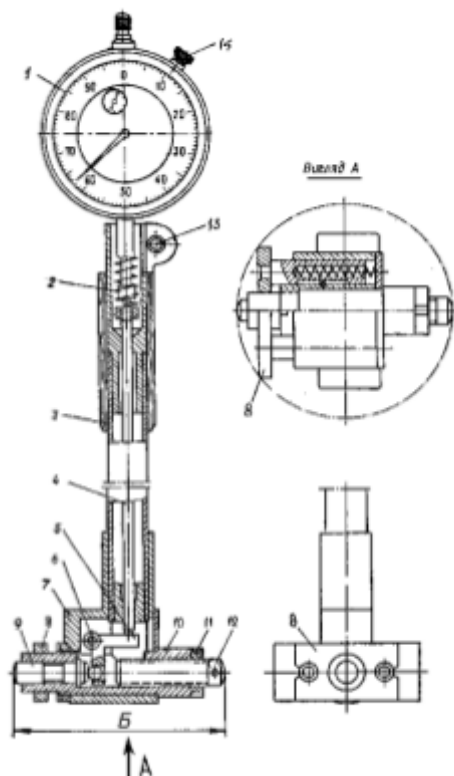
Індикаторний нутромір: 1 – індикаторна головка; 2 – вимірювальний стрижень індикатора; 3 – трубка корпусу; 4 – проміжний вимірювальний стрижень; 5 – дво-плечий Г-подібний важіль; 6 – вісь двоплечого важеля; 7 – корпус; 8 – центрувальний місток; 9 – рухомий вимірювальний стрижень; 10 – трійник; 11 – контргайка; 12 – переставний вимірювальний стрижень; 13 – затискний гвинт індикатора; 14 – стопорний гвинт обичайки
